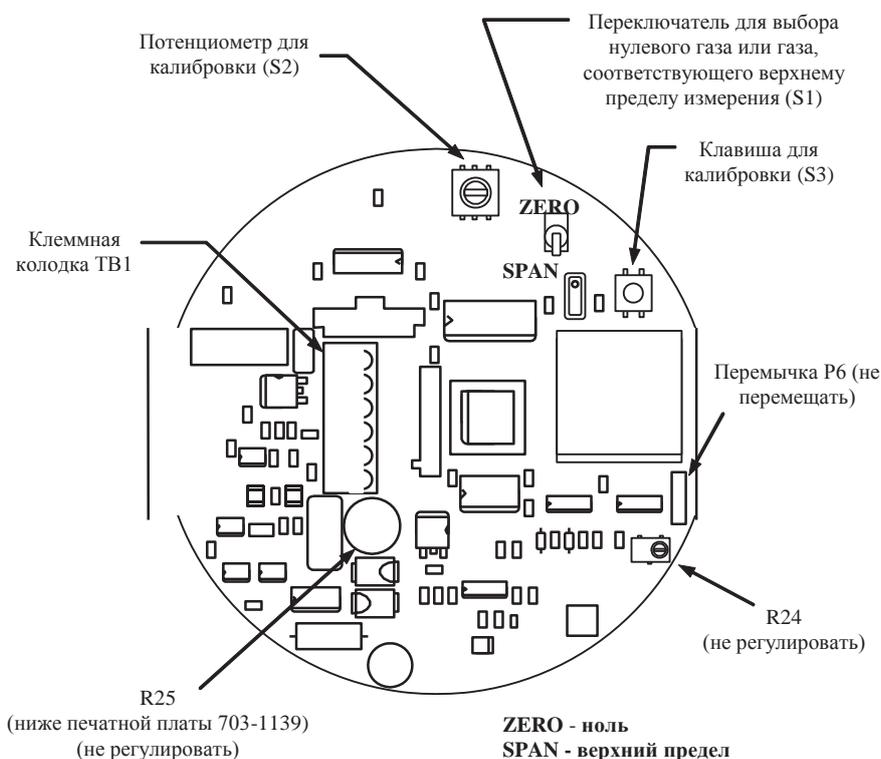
Расположение калибровочных переключателей на печатной плате 703-1139
